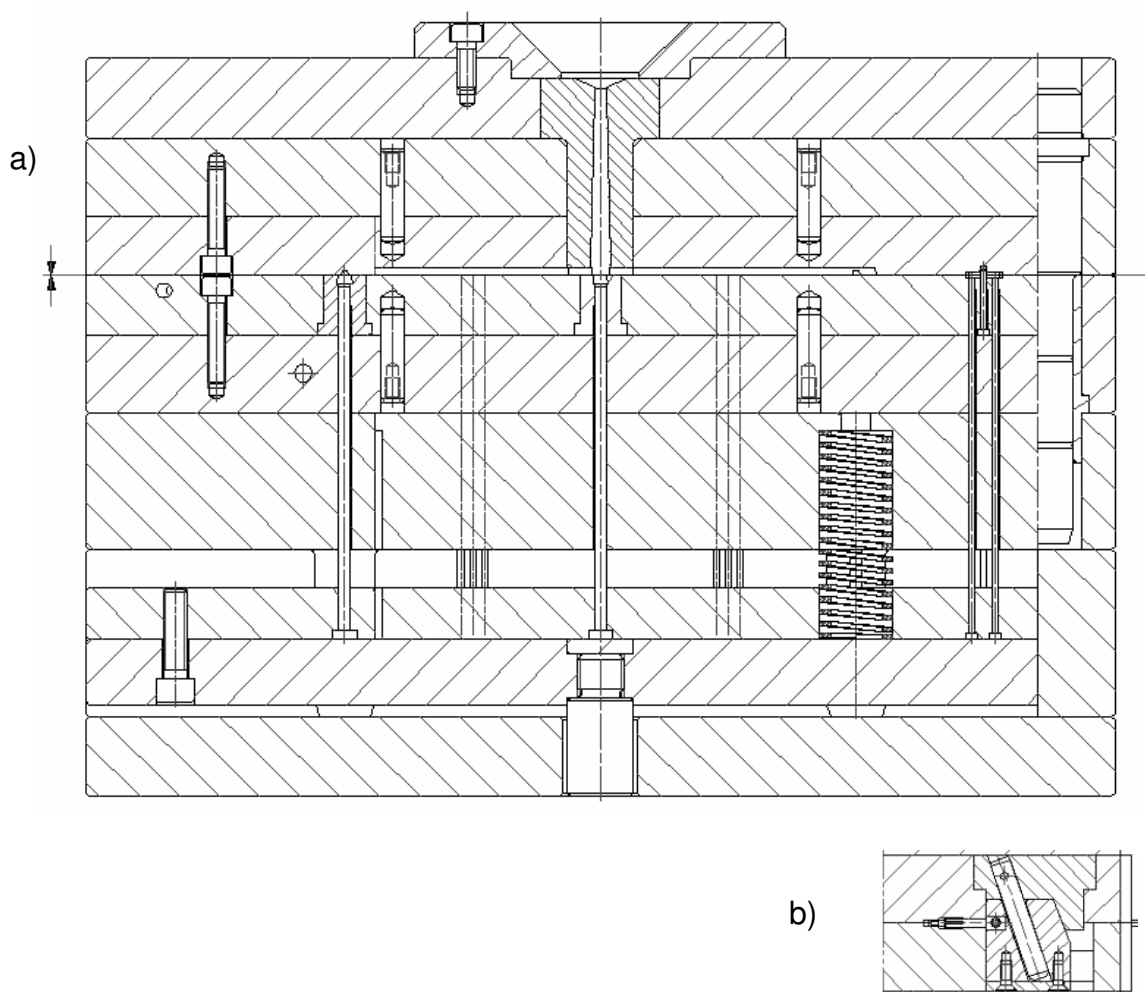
Molde para injetar a unidade representativa dos grupamentos amina e carboxila: (a) desenho técnico em corte da montagem; (b) detalhe construtivo necessário para criar os furos em ângulos das unidades
